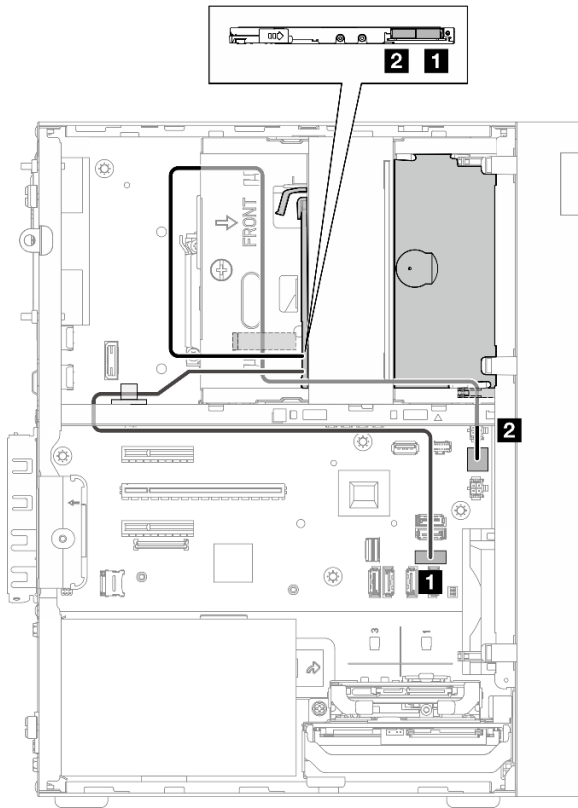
Kabelführung für optisches Plattenlaufwerk
